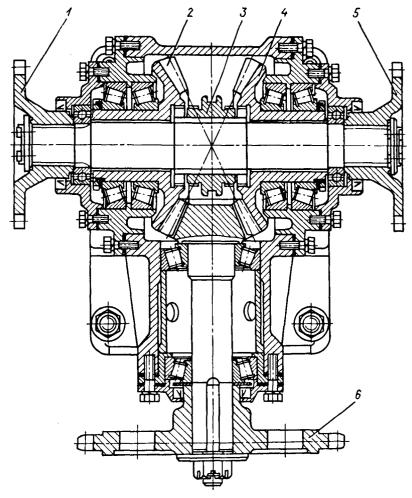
Редуктор привода конвейера экскаватора ЭР-7АМ
